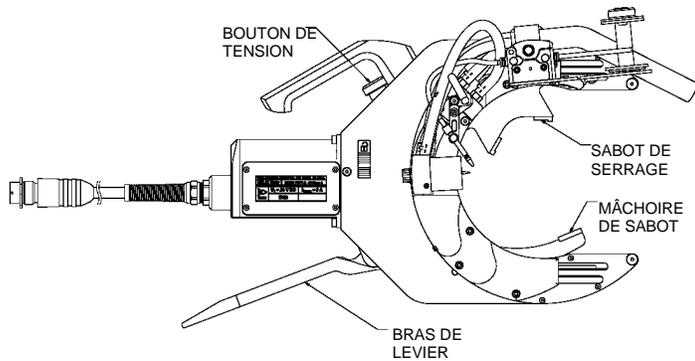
Ensemble du corps, mécanisme de serrage
